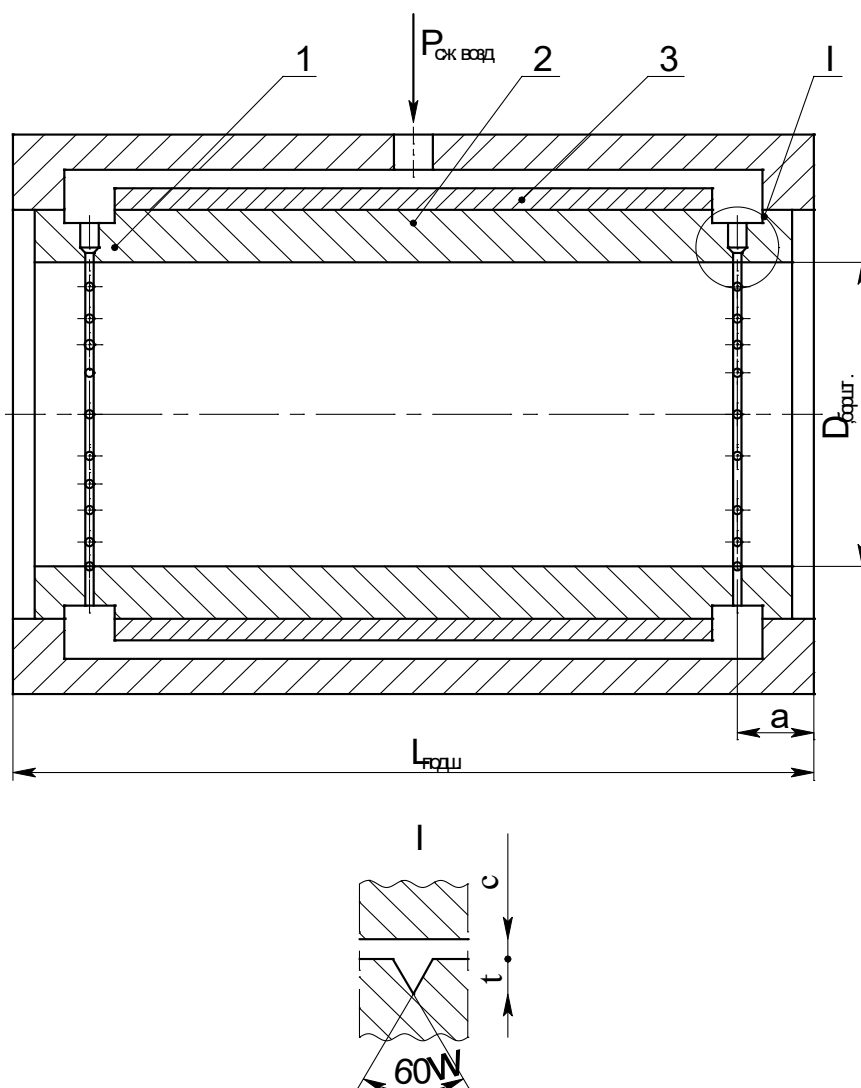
Типовая цилиндрическая опора: 1 – вкладыш, 2 – борштанга, 3 – опора
